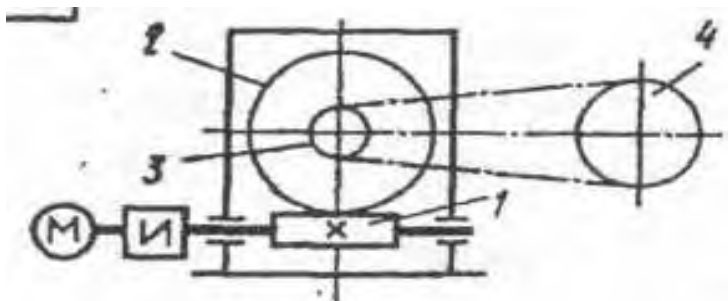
Кинематическая схема привода с открытой цепной передачей:
